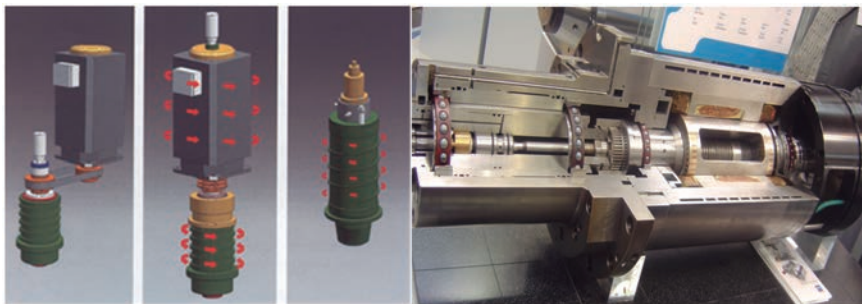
Izda. Las tres formas de conexión motor y husillo en máquina herramienta. Dcha. Corte de un electrohusillo: muestra rodamientos, motor y canales de refrigeración (ranuras rectangulares en periferia).
